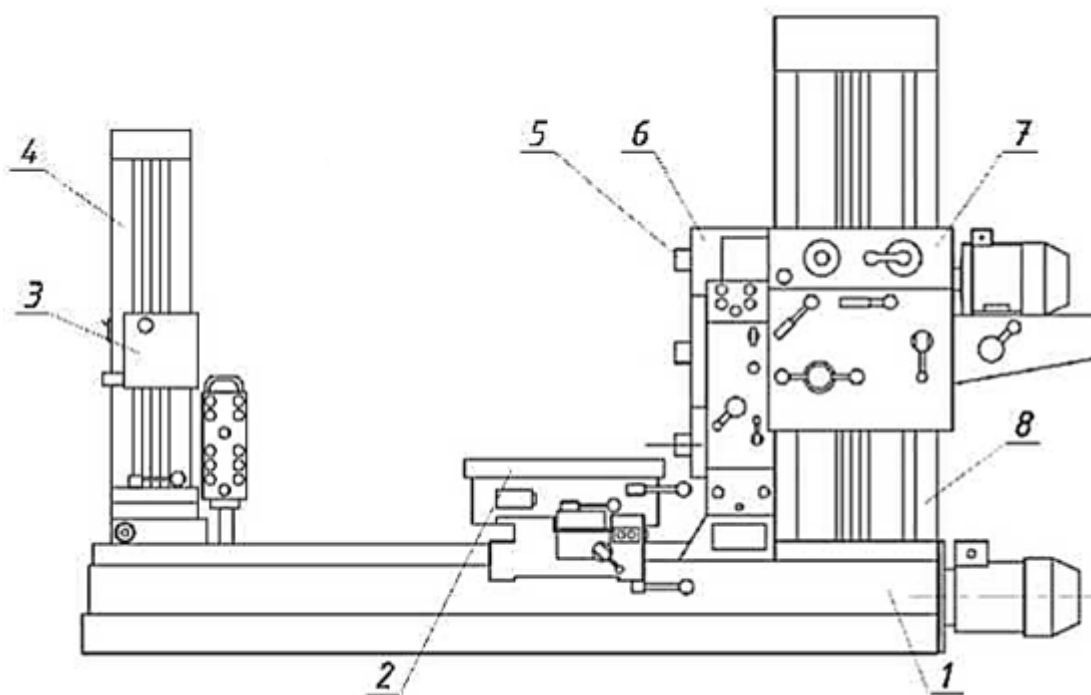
Загальний вигляд горизонтально-розточувального верстата
